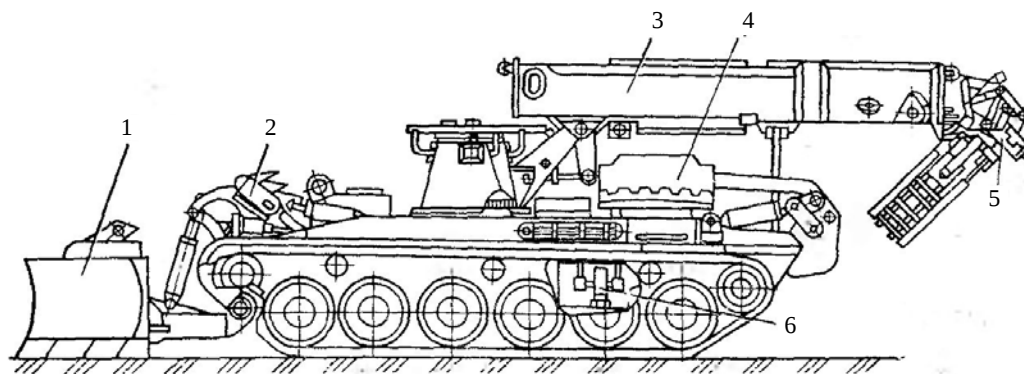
Рабочее оборудование инженерной машины разграждения ИМР-2М: 1 – универсальный бульдозер; 2 – ножевой колеино-минный трал; 3 – полноповоротная телескопическая стрела; 4 – скребок-рыхлитель; 5 – манипулятор; 6 – редуктор привода насосов
